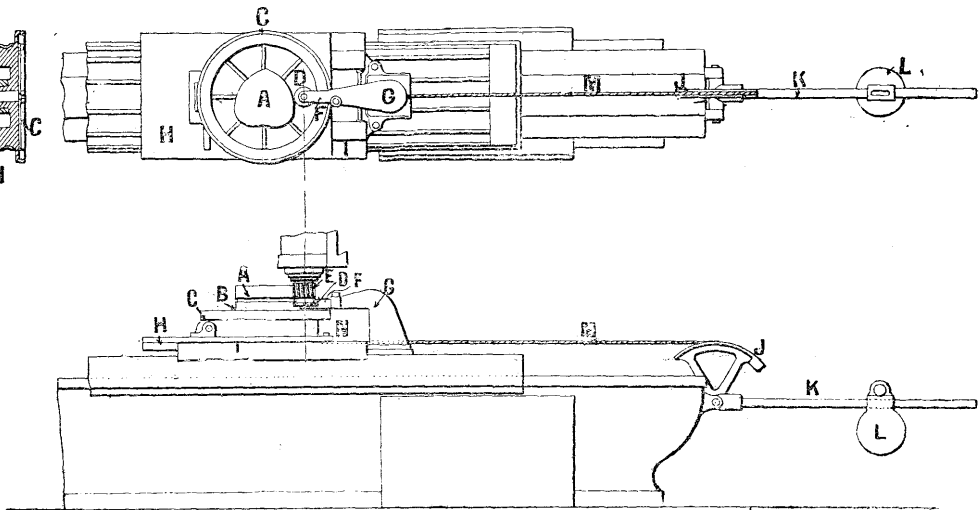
Appareil pour le fraisage de la Ingersoll Milling Machine Company, de Rockford (E.-U.).
